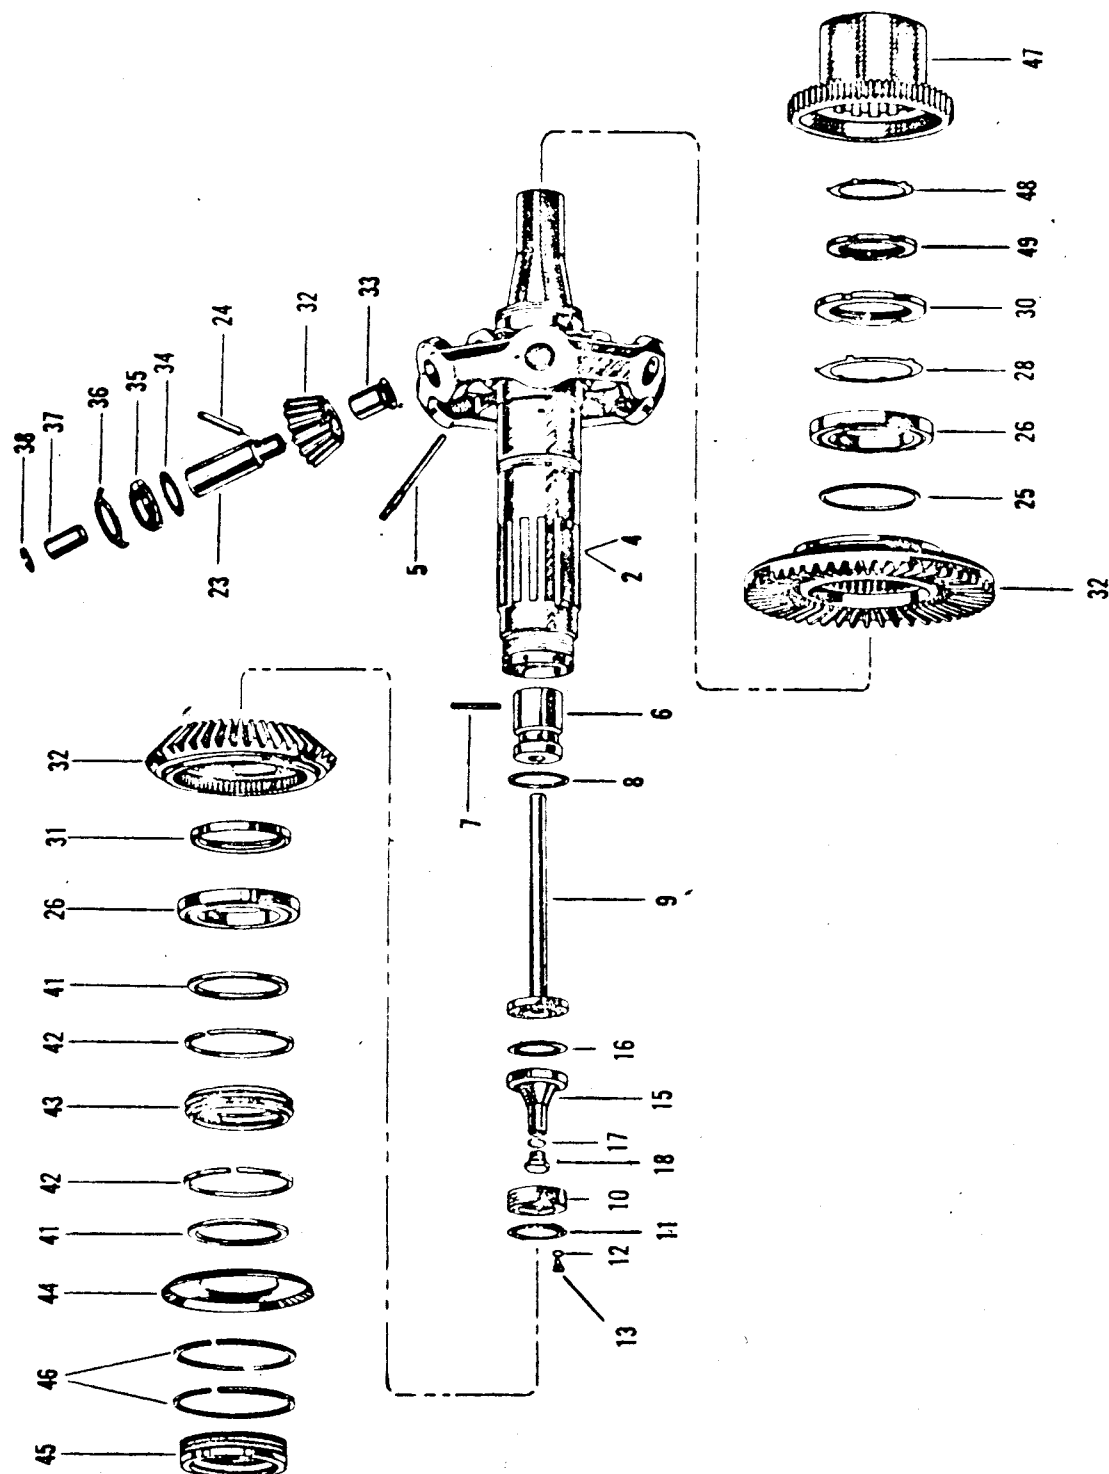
ENGRENAGES RÉDUCTEUR SC3G
